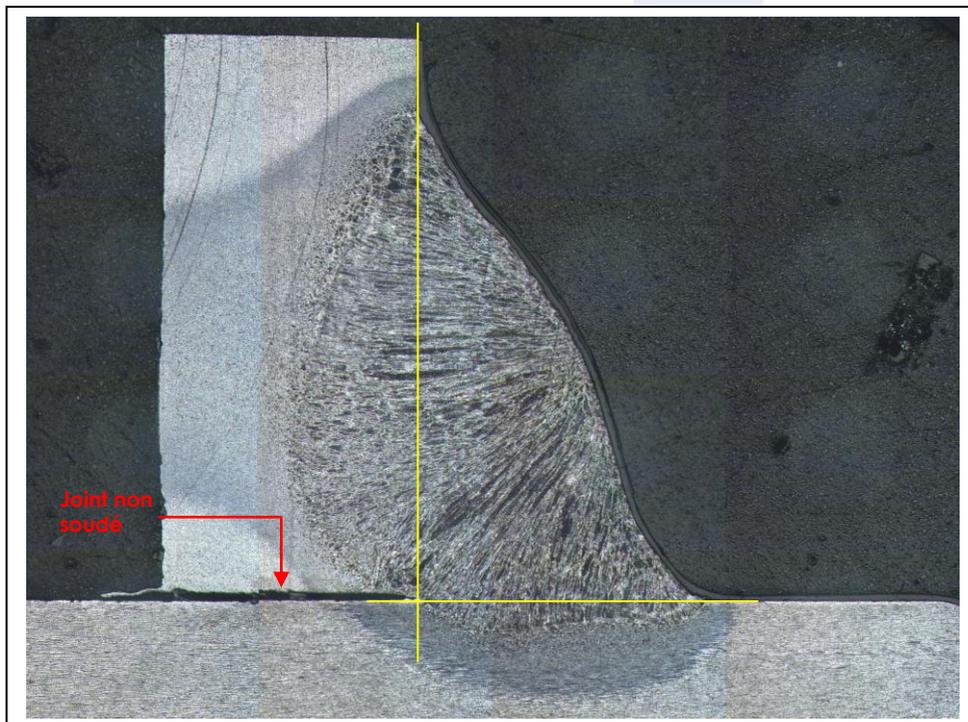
Absence de fissure du cordon de soudure 1DE - surface ext.
